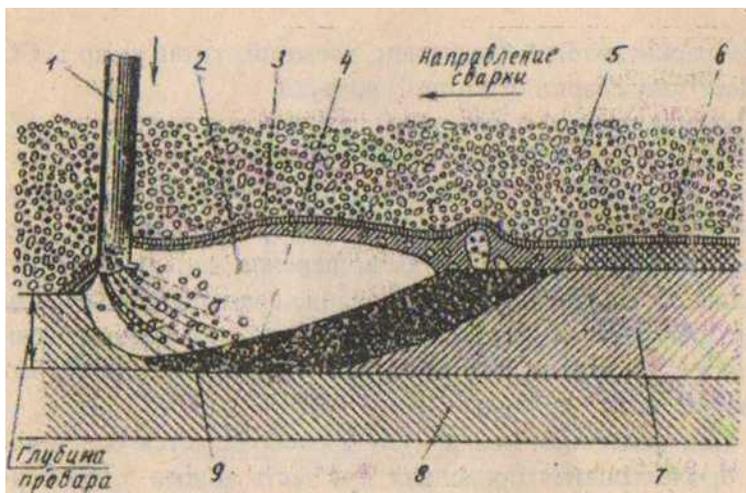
Схема горения сварочной дуги под флюсом
